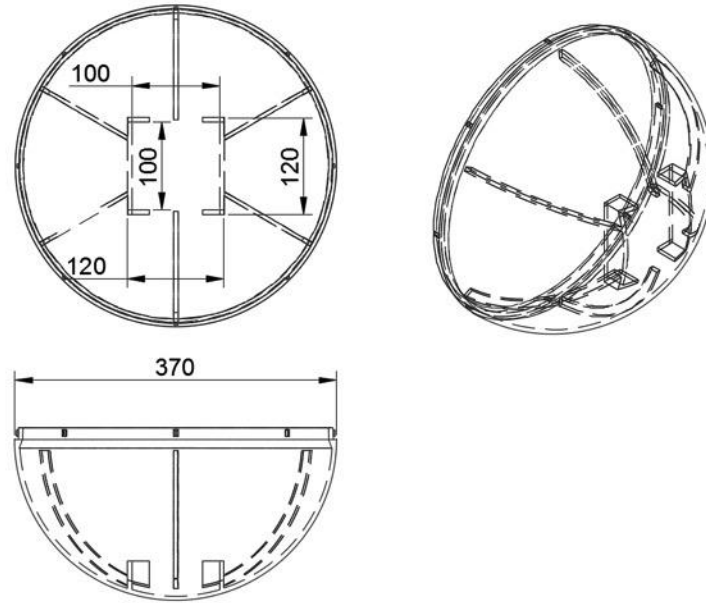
Diseño CAD para la manufactura aditiva de la esfera.
